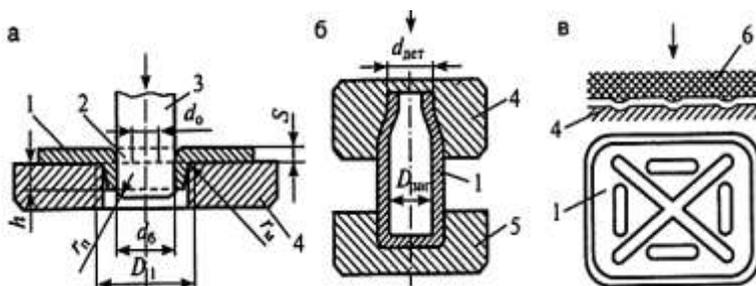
Схемы формообразующих операций: а – отбортовка; б – обжим; в – формовка. 1 – изделие; 2 – заготовка; 3 – пуансон; 4 – матрица; 5 – подставка-упор; б – резиновая подушка
